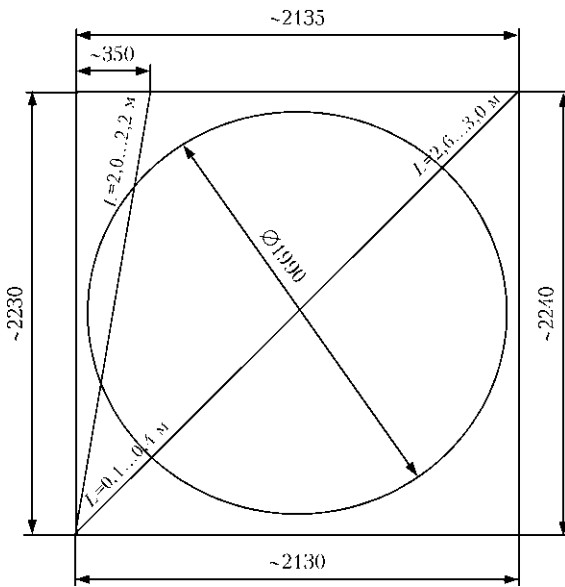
Схема разметки биметаллической заготовки из стали 09Г2С + титан Вt1-0 под вырезку трубной доски и образцов для исследования
